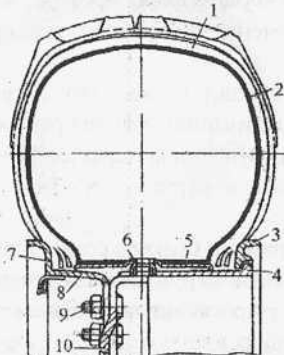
Шина с регулируемым давлением воздуха: 1 – покрывка; 2 – камера; 3 – бортовое кольцо; 4 – внутренняя часть обода; 5 – распорное кольцо; 6 – направляющая вентиля; 7 – закраина обода; 8 – наружная часть обода; 9 – шпилька крепления обода; 10 – диск колеса
